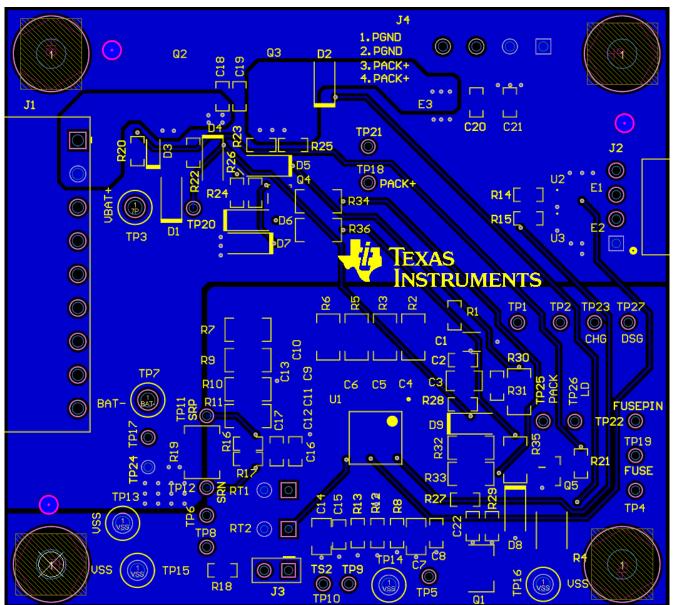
BQ76942 Example Board Layout—Bottom Layer
